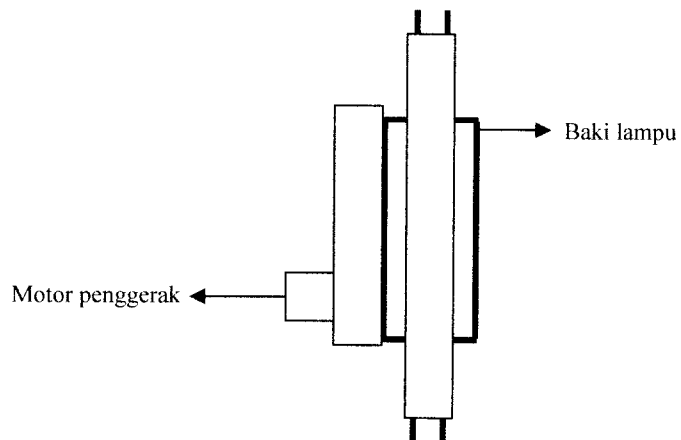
Penjepit elektroda lampu tampak samping depan
